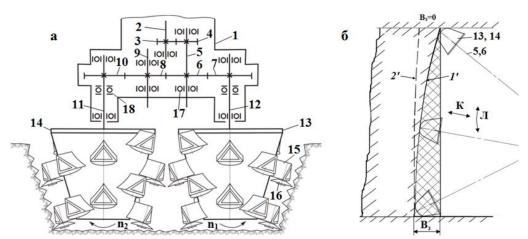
Исполнительный орган проходческого комбайна с двумя радиальными реверсивными коронками: а – конструктивно-кинематическая схема; б – схема зарубки
